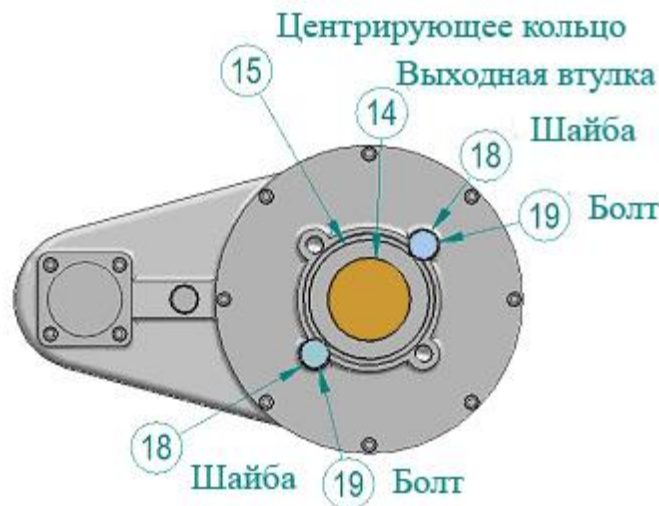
А. Редуктор IS с установленными шайбами и болтами
